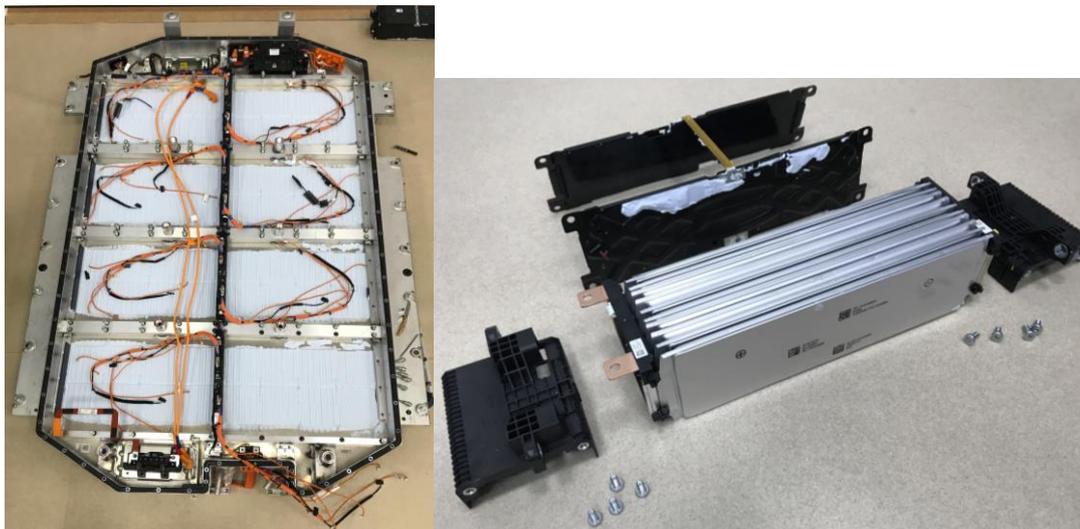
Корпус и submodule тяговой аккумуляторной батареи
